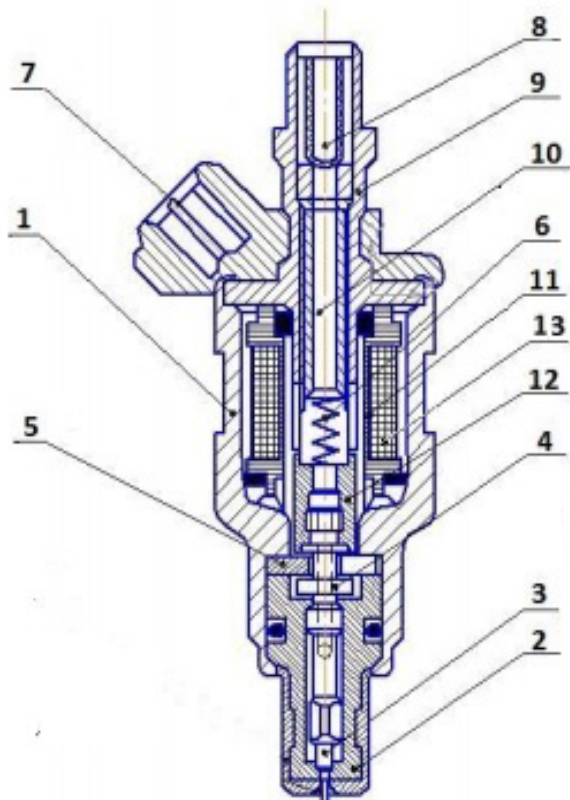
Устройство форсунки для впрыска бензина: 1 – корпус; 2 – распылитель; 3 – клапан; 4 – упорный бурт; 5 – упорная шейка; 6 – пружина клапана; 7 – разъем; 8 – предохранительный фильтр; 9 – штуцер; 10 – регулировочный винт пружины; 11 – сердечник электромагнита; 12 – якорь электромагнита; 13 – катушка электромагнита
